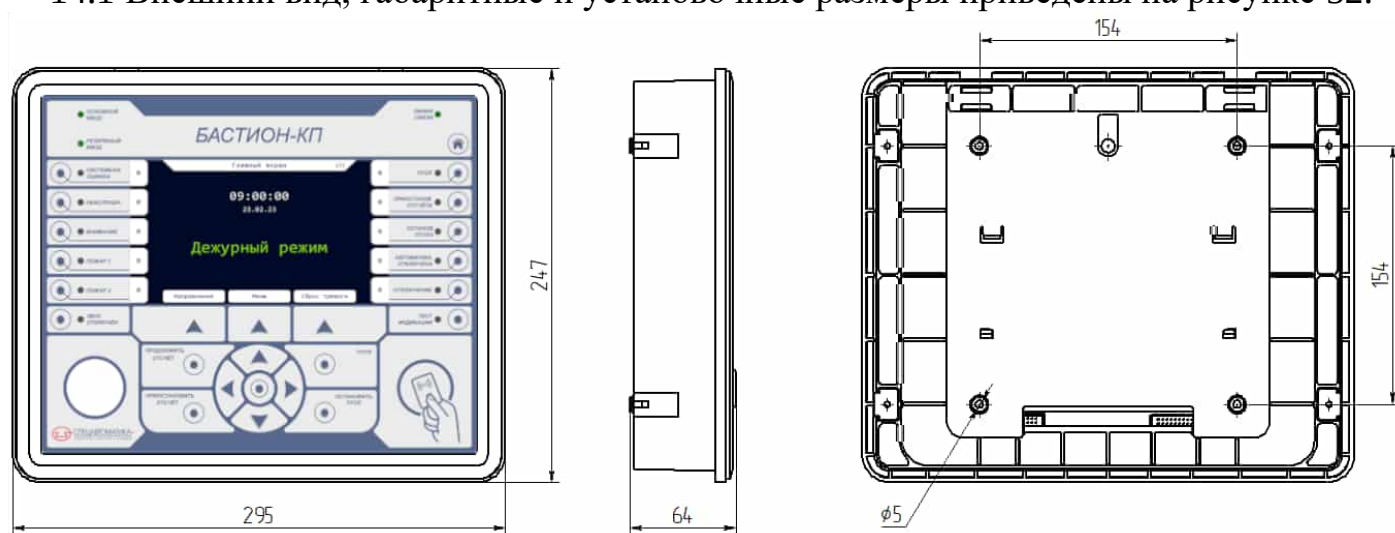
Внешний вид, габаритные и установочные размеры
